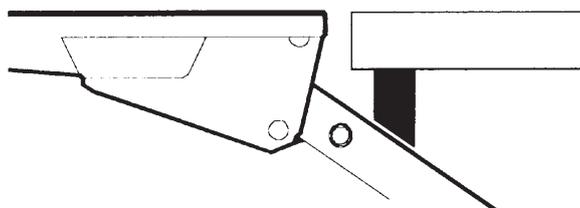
Placez les butées d'arrêt entre les bras de levage et la traverse arrière du plancher
